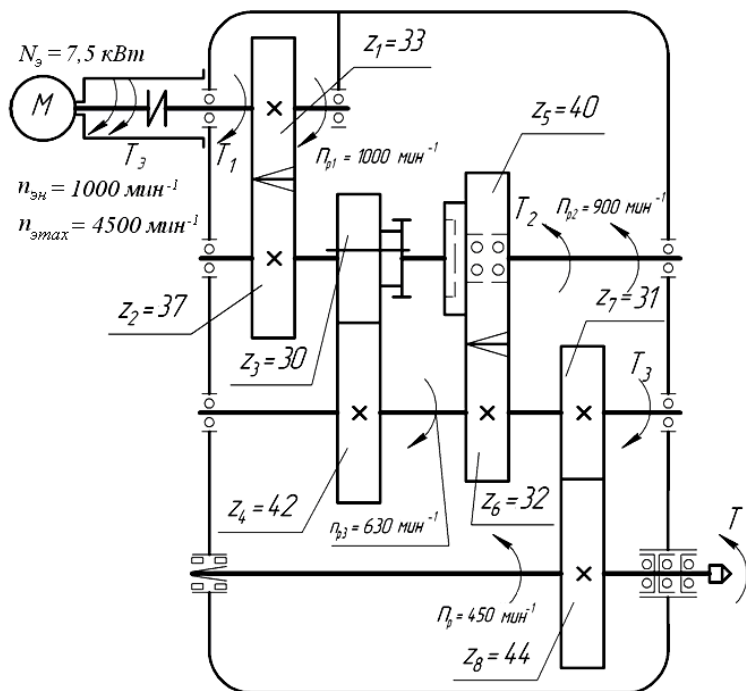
Кинематическая схема шпиндельной бабки с двухступенчатой коробкой скоростей с расчетными частотами и крутящими моментами на валах станка с ЧПУ
